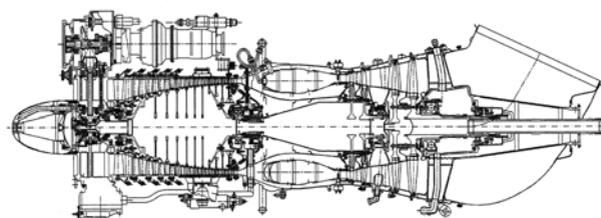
Продольный разрез газотурбинного двигателя ТВЗ-137
